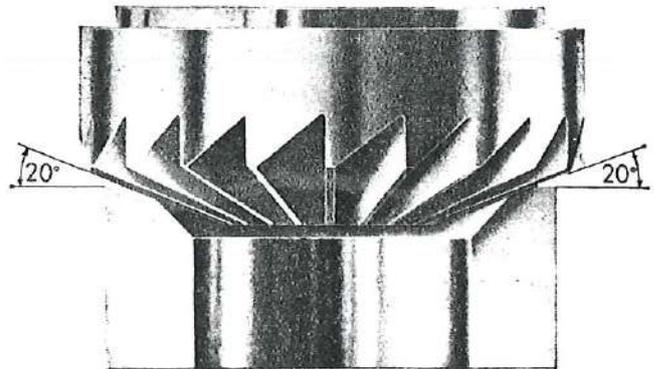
Reducción del asiento de válvula en su parte superior, con fresa de 20°
